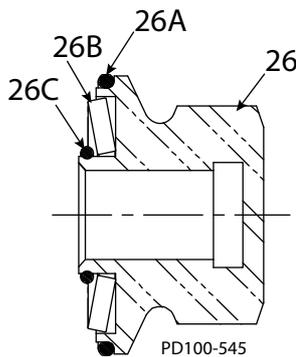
Corte transversal do conjunto de porcas do rotor, conforme montado
